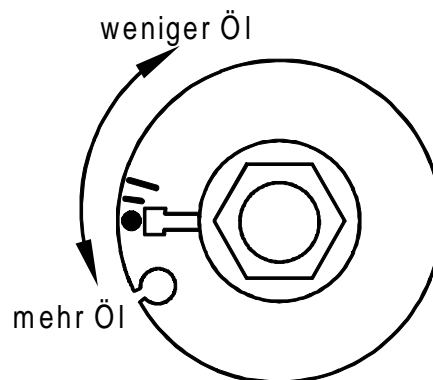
Ansicht der Pumpenscheibe bei Vollgas
